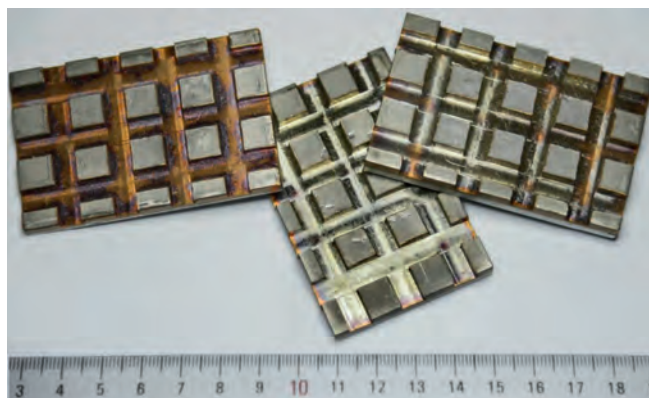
Диффузионная сварка Cu+Al16
